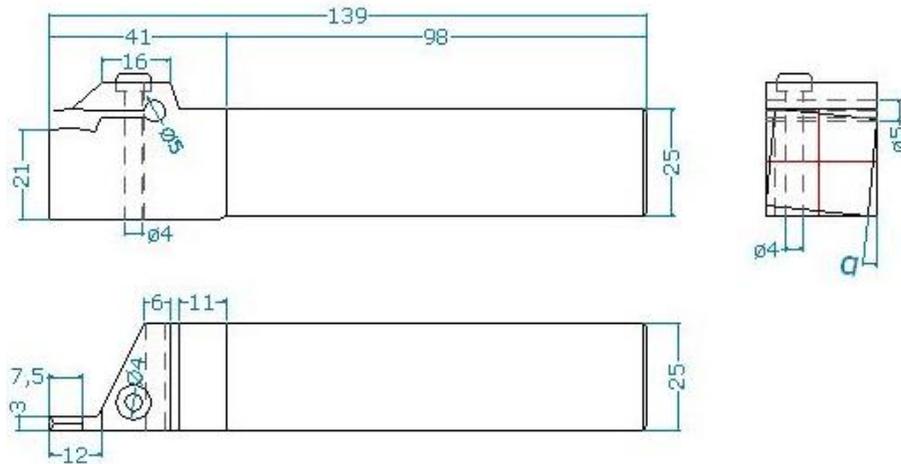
Herramienta propuesta para creado del tornillo sin fin en torno CNC
